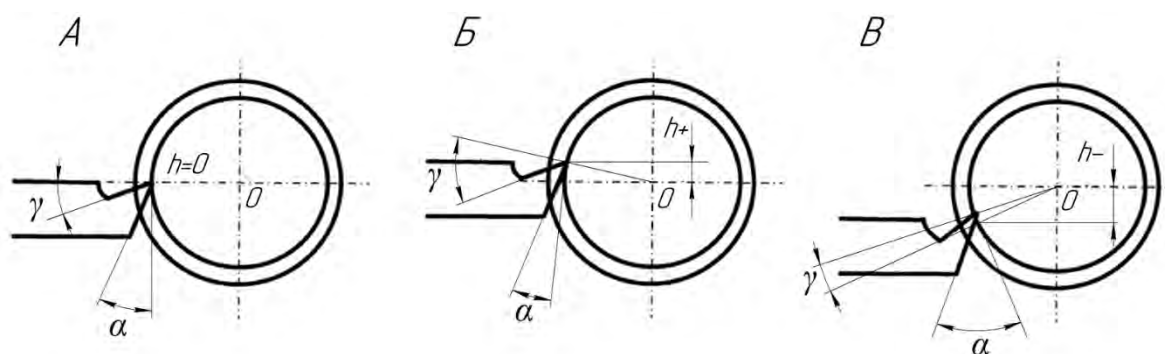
Изменение углов при установке токарного проходного резца по высоте заготовки (а), выше (б) и ниже (в) оси заготовки
